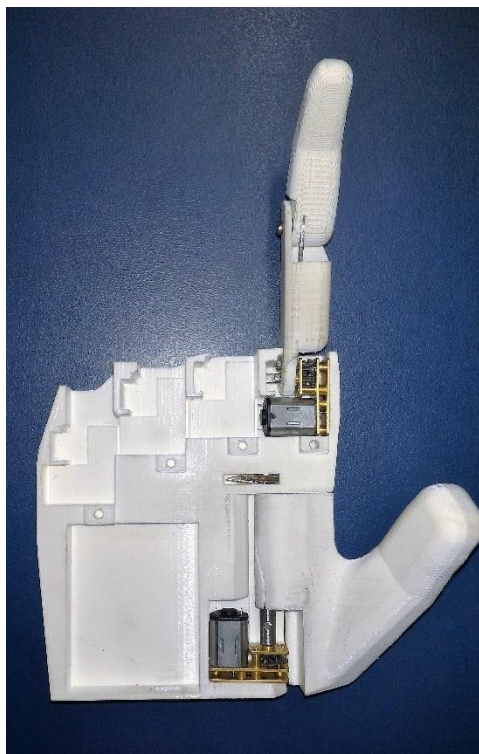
Montagem conjunto dedo indicador e região palmar.
